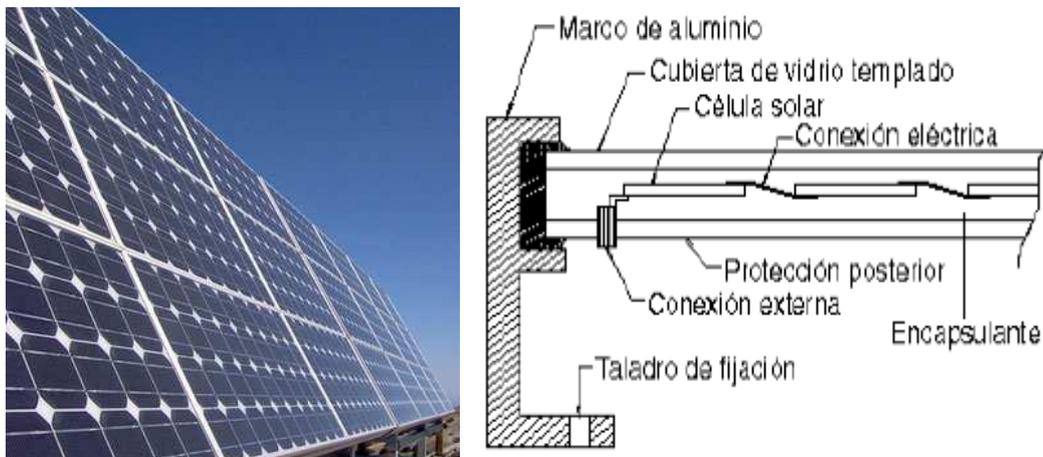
Aspecto Físico y Principales Partes de un Panel Fotovoltaico
